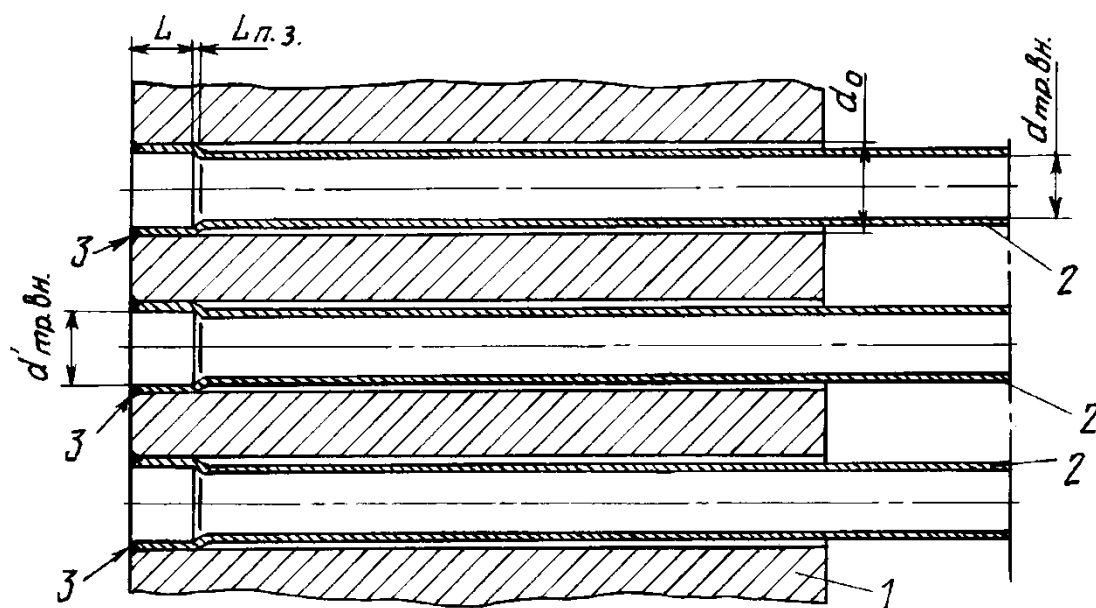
Закрепление труб в трубной доске при помощи сварки взрывом
